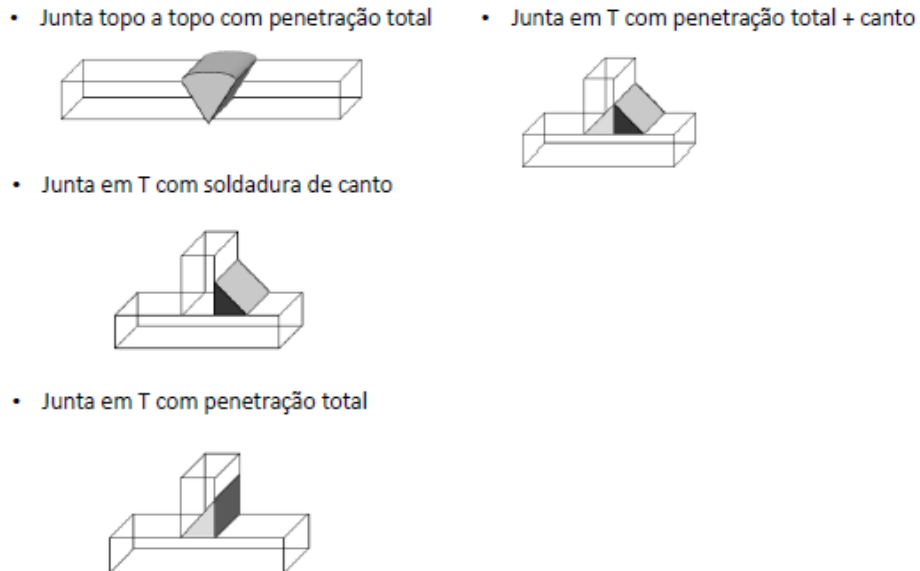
Exemplos de juntas soldadas [4]
